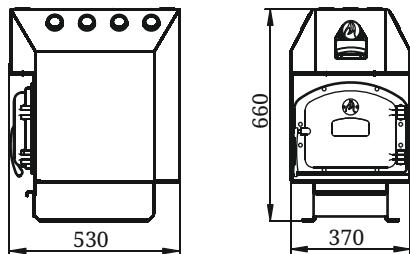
Габаритные размеры печи «Студент» с выходом трубы вверх
